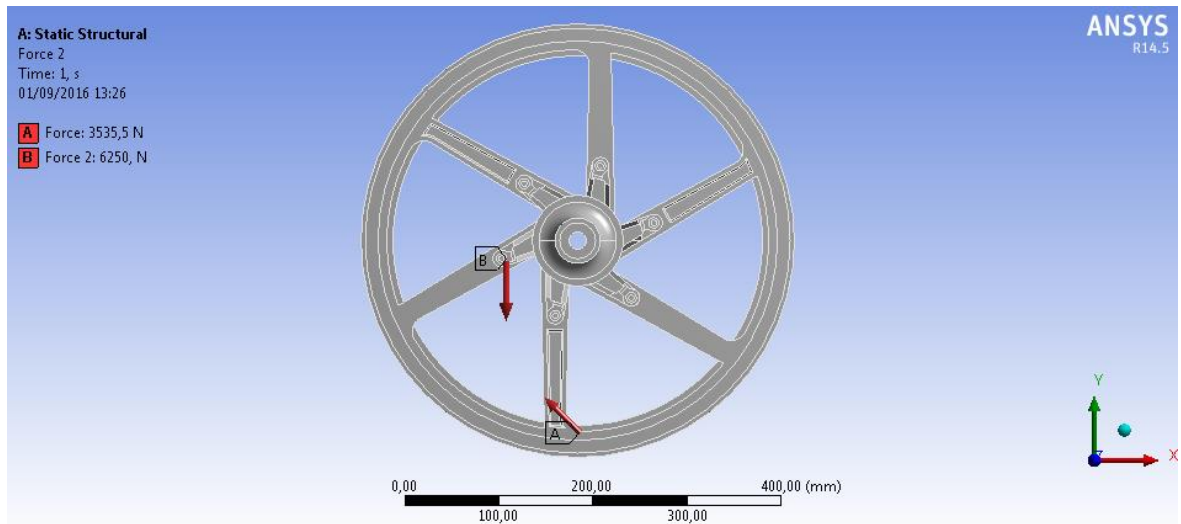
Adición de carga en torreta izquierda en el diseño original. Fuente: Propia
